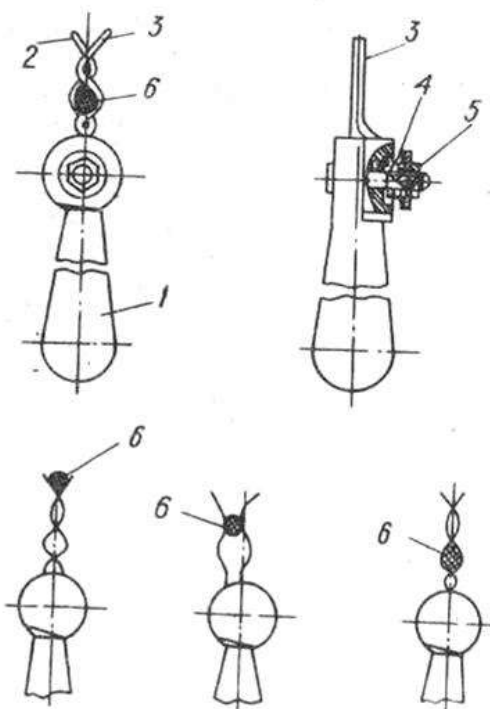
Приспособление для сбора ягод: 1 – держатель; 2 и 3 – губки; 4 – пружина; 5 – гайка регулировочная; 6 – плодоносящая ветка
